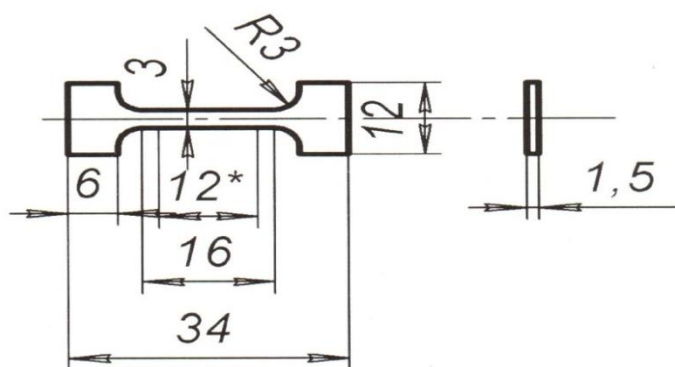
Чертеж образца для механических испытаний на растяжение
